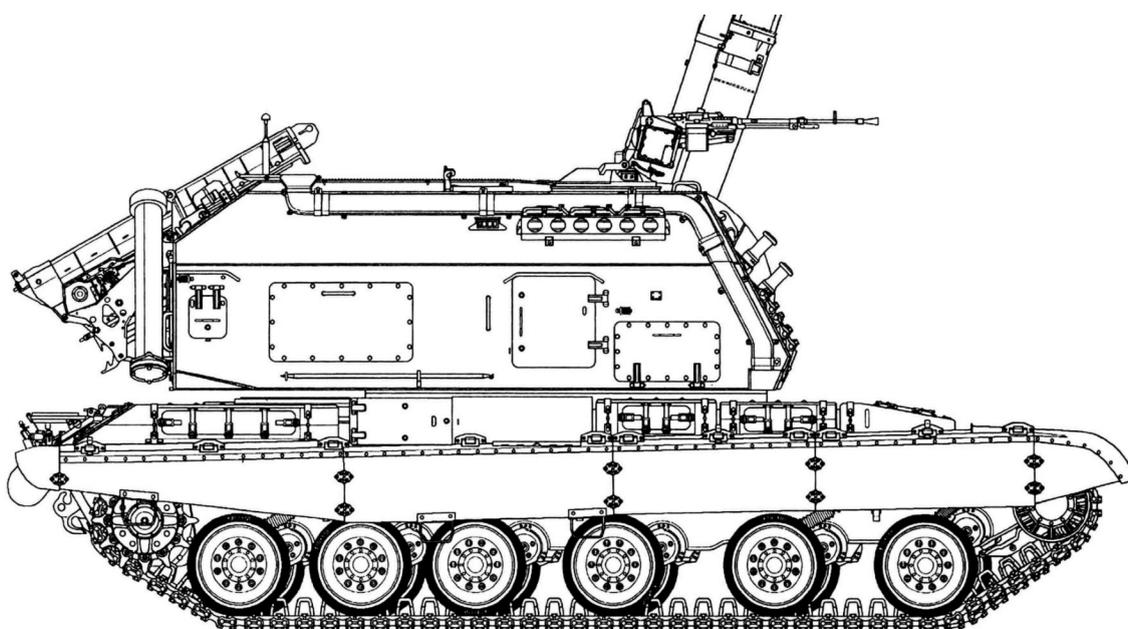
Чертеж СГ 2С19 (вид справа)
